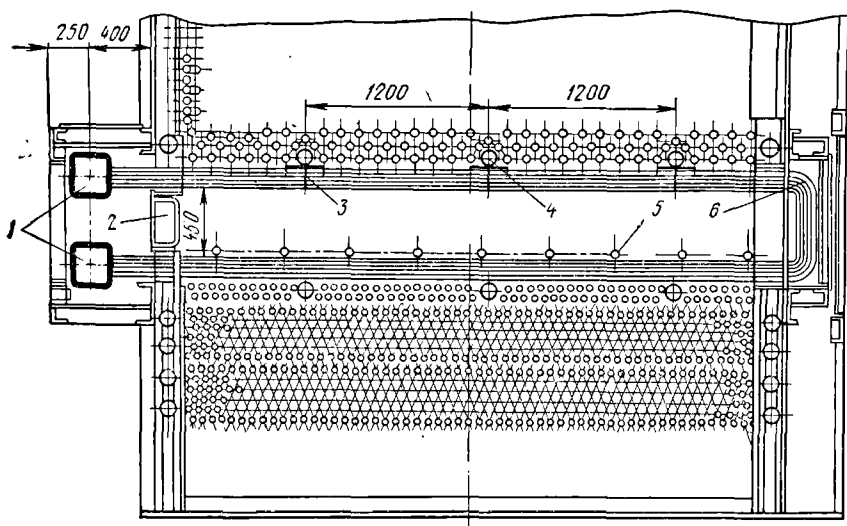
Установка горизонтального петлевого пароперегревателя в пучке труб котла
